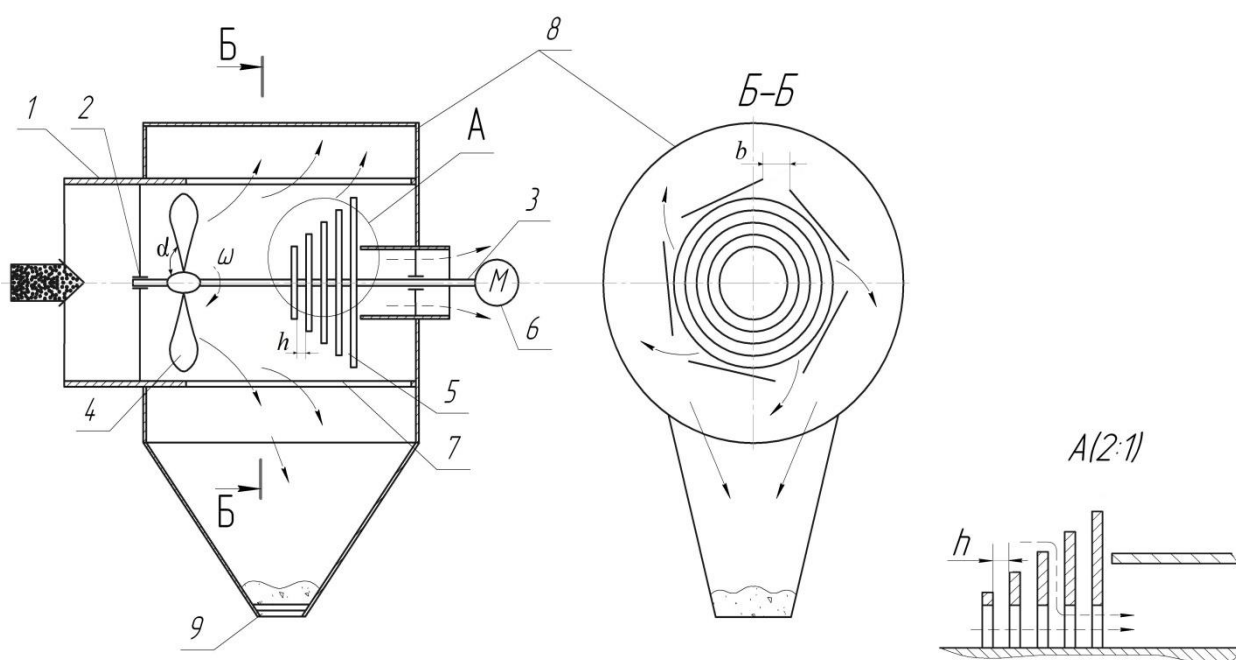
Конструктивная схема разработанного циклона с многодисковым доочистителем: 1 – цилиндрический корпус, 2 – опоры; 3 – вал; 4 – завихритель; 5 - многодисковый доочиститель; 6 – электродвигатель; 7 – жалюзи; 8 – пылесадочная камера; 9 - шлюзовой затвор; – движение запылённого воздушного потока; – дисперсных частиц; – очищенного воздушного потока
